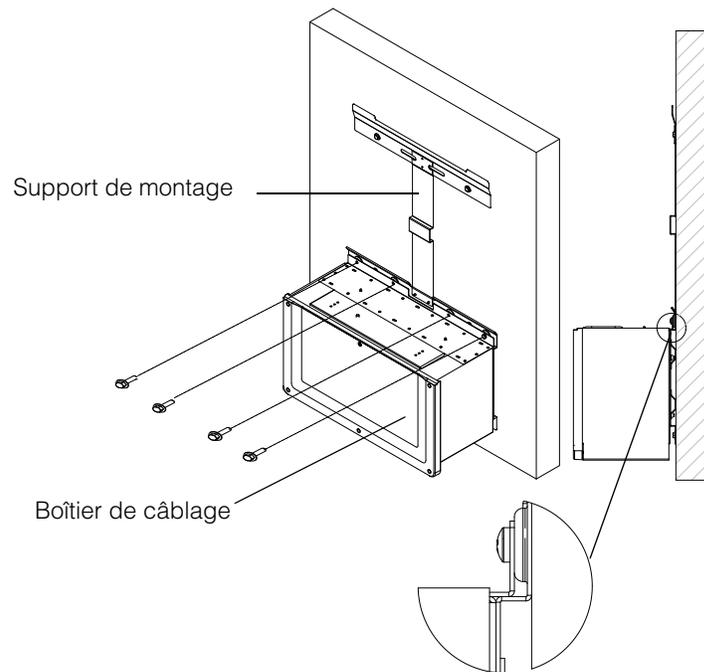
Fixation du boîtier de câblage sur le support de montage
